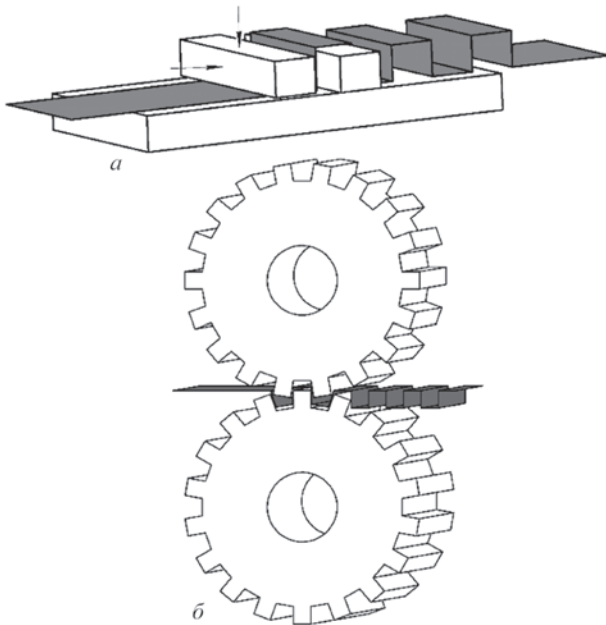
Схема формирования полос сотового заполнителя с помощью прямоугольных вкладышей (а) или зубчатой передачи (б)
